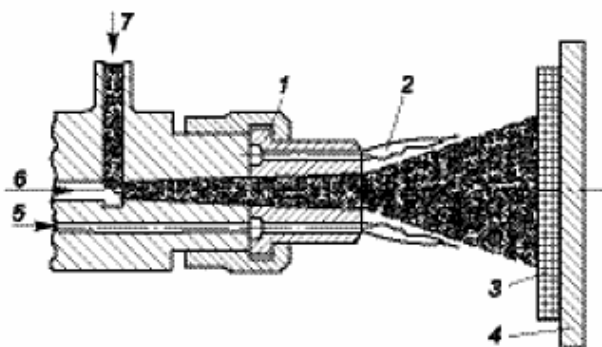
Схема газопламенного напыления с материалом порошкового типа: 1 – газовое сопло; 2 – кольцевое пламя; 3 – покрытие; 4 – подложка; 5 – горючий газ; 6 – кислород; 7 – порошок
